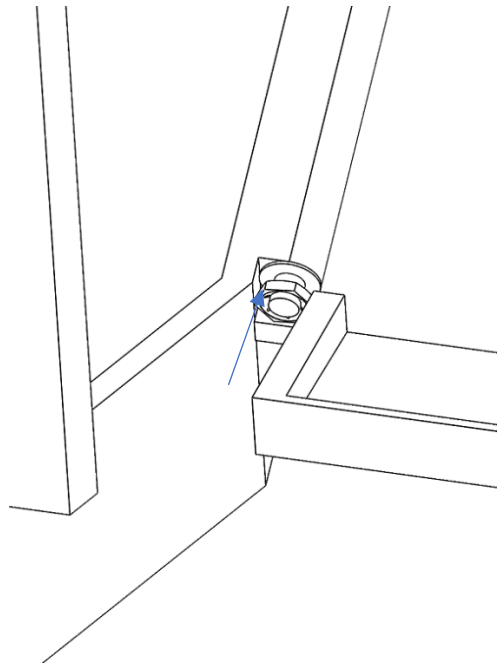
Secuencia 8. Ensamblaje subconjunto 1.1
